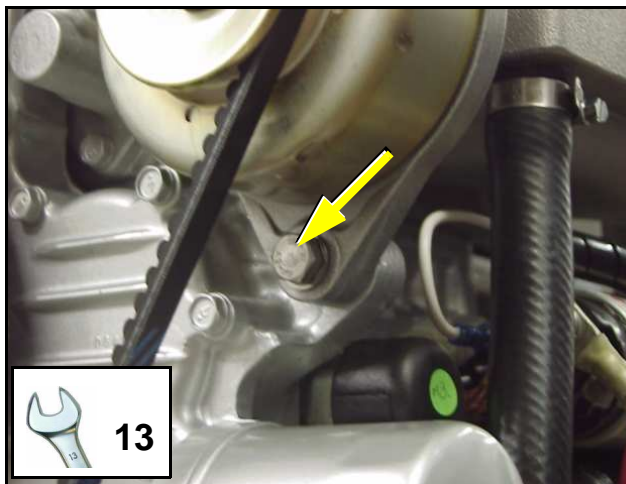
Schraube unter der Lichtmaschine
